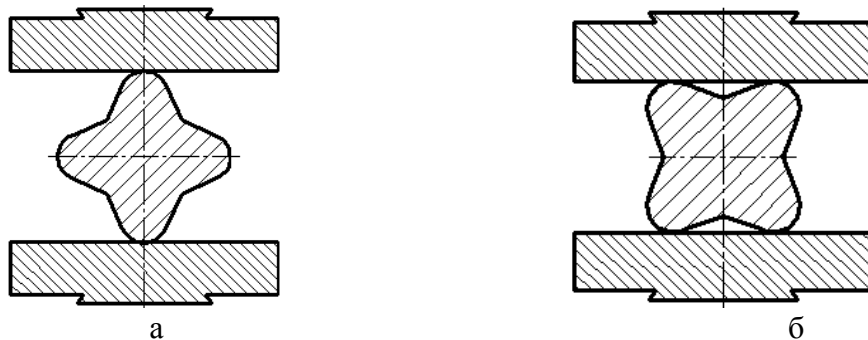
Схемы ковки четырехлучевой заготовки плоскими бойками: крестом (а) и иксом (б)
